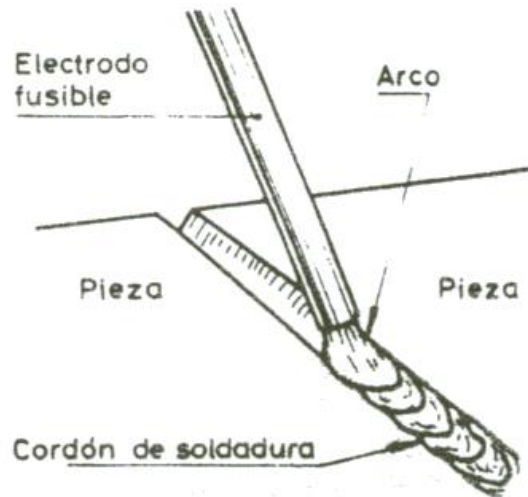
Esquema del proceso de la formación del cordón de soldadura en el arco eléctrico.
